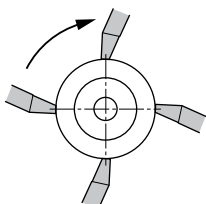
Проверка осевой выверки при помощи штангенциркуля — контроль по периметру
